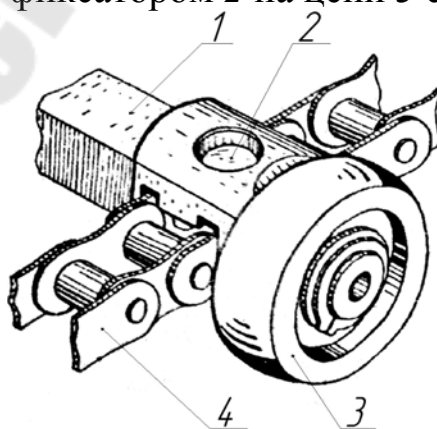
Механизм прессующий: 1 – планка (скалка); 2 – фиксатор; 3 – цепь; 4 – опора роликовая (каток)
